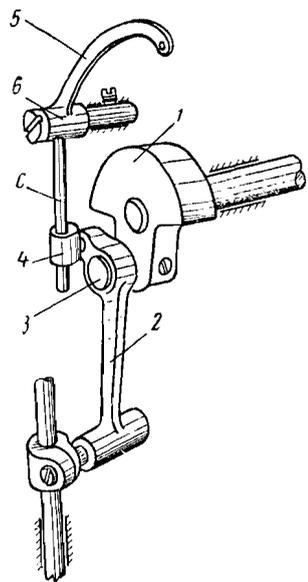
Кулисный механизм нитепритягивателя машины 24-го класса
